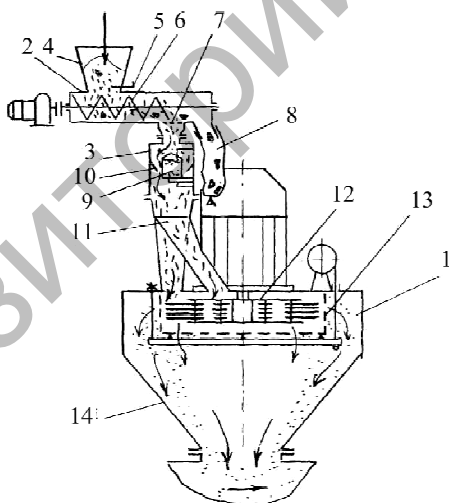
Схема рабочего процесса дробилки закрытого типа с вертикально расположенной рабочей камерой:
